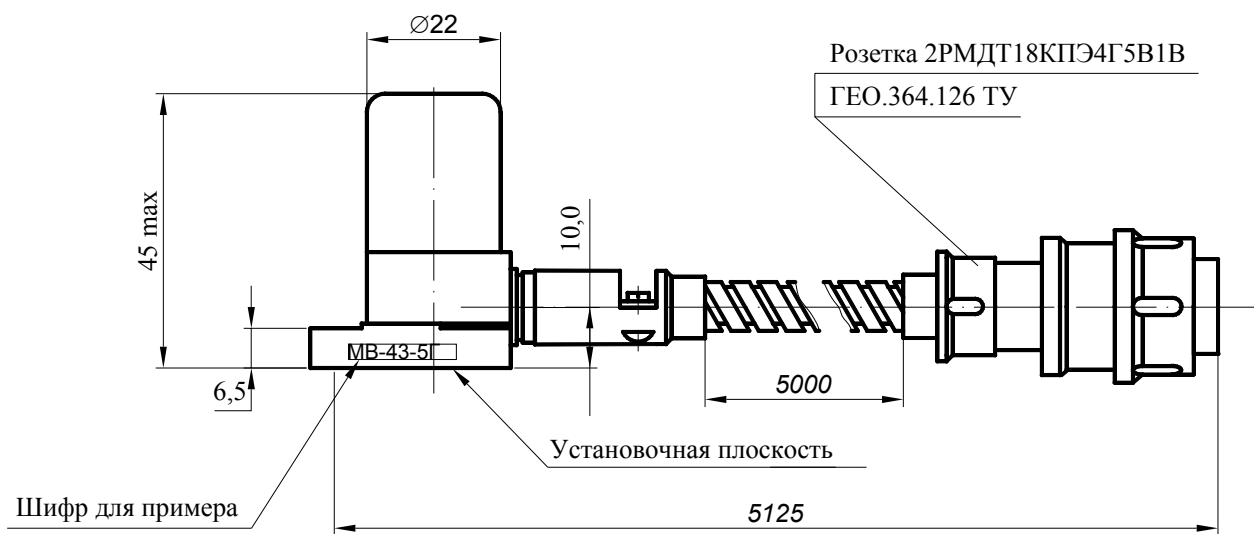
Габаритно-установочные размеры вибропреобразователя MB-43-5Г/5,0
